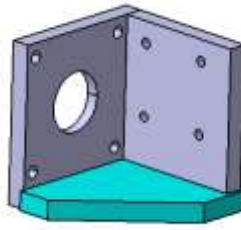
Muntatge dels suport motor pas a pas (Farran, E.)
